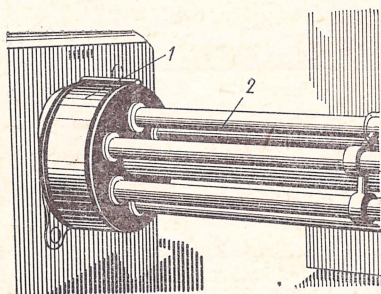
Шумозащитный кожух к токарному станку-автомату
